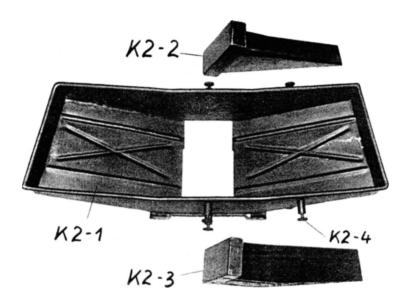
Gurtfüller 151; Trichter, Einzelteile
